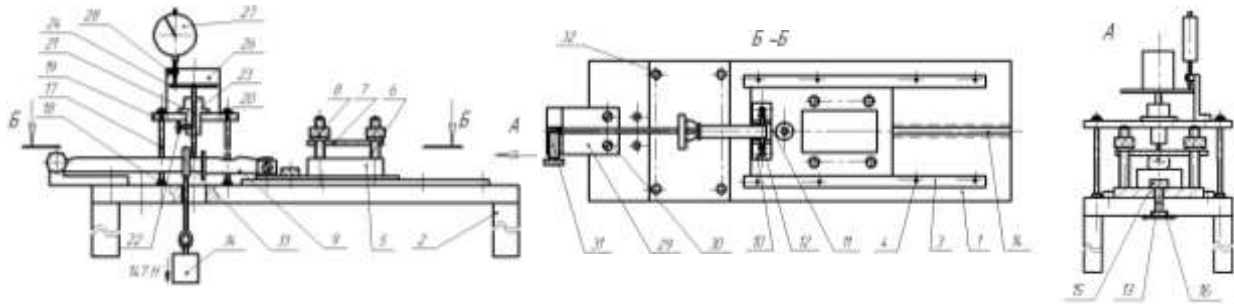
Схема налагодження пристрою для визначення міцності конструкції вузла фіксатора клинка: 1 – корпус; 2 – ніжки; 3 – напрямні; 4 – гвинти; 5 – рухомий столик; 6 – шпильки; 7 – пластина; 8 – гайки; 9 – руків'я; 10 – опорний елемент; 11 – гвинт; 12 – гвинт регулюючий; 13 – болт стопорний; 14 – Т-подібний паз; 15 – гайка; 16 – пластина; 17 – стойка; 18 – гайка; 19 – пластина; 20 – гайка; 21 – напрямна; 22 – гвинт стопорний; 23 – вимірювальний штир; 24 – пластина; 26 – опора; 27 – вимірювальний прилад; 28 – гвинт; 29 – кронштейн; 30 – гвинт; 31 – гвинт; 32 – різьбові отвори; 33 – хомут; 34 – вага
